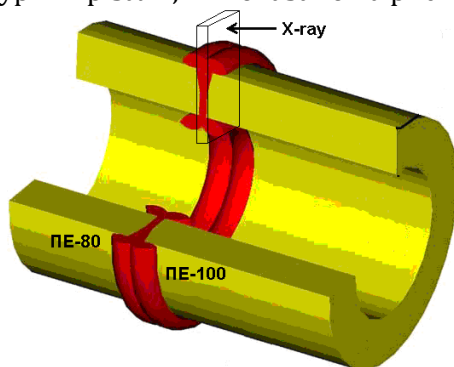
Модель зварного з'єднання поліетиленових труб із різнотипних поліетиленів PE-100 та PE-80
